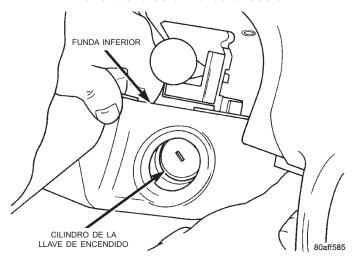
Desmontaje de la funda inferior del cilindro de la llave de encendido
